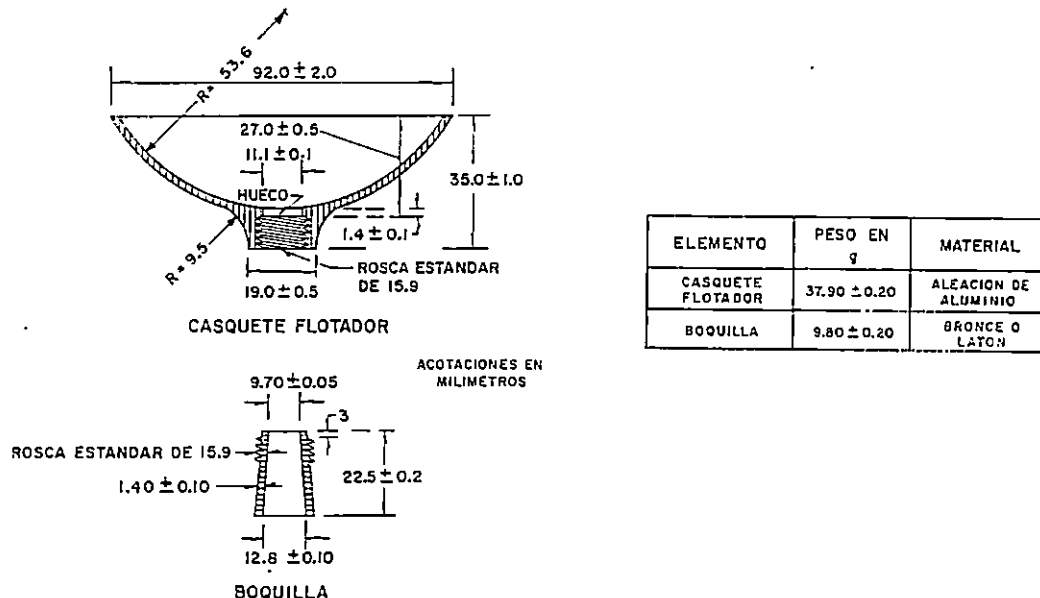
Dimensiones del Casquete y Boquilla o Collar para la realización del ensayo de flotación.
